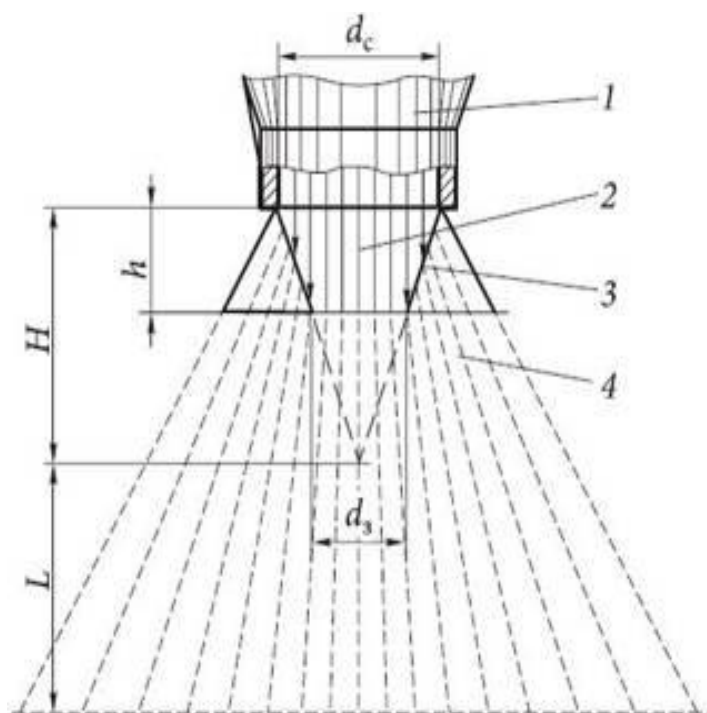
Схема истечения защитного газа из сварочного сопла[23]:
